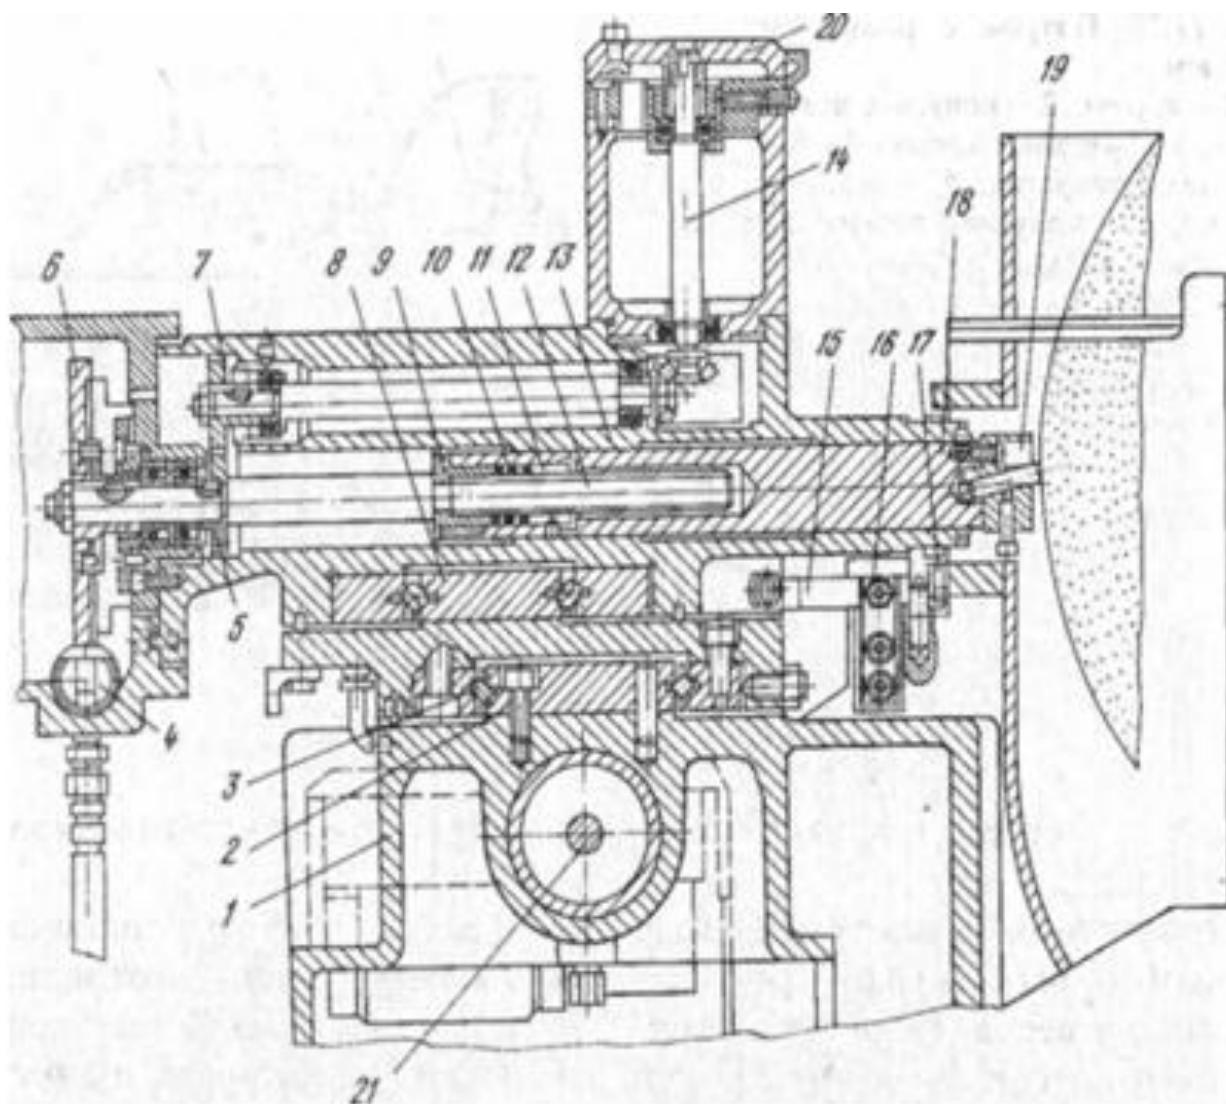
Прибор для автоматической правки шлифовального круга станка модели ЗМ151: 1 – корпус, 2 – продольные направляющие. 4 – каретка, 5, 7 – зубчатые колеса, 6 – храповое колесо, 8 – поперечные направляющие, 9, 11 – полугайки, 10 – пружина, 12 – ходовой винт, 13 – суппорт, 14 – вал, 15 – копир, 16, 17 – винты тонкой регулировки копира, 18 – пиноль, 19 – алмазодержатель, 20 – маховичок, 21 – шток гидроцилиндра.
